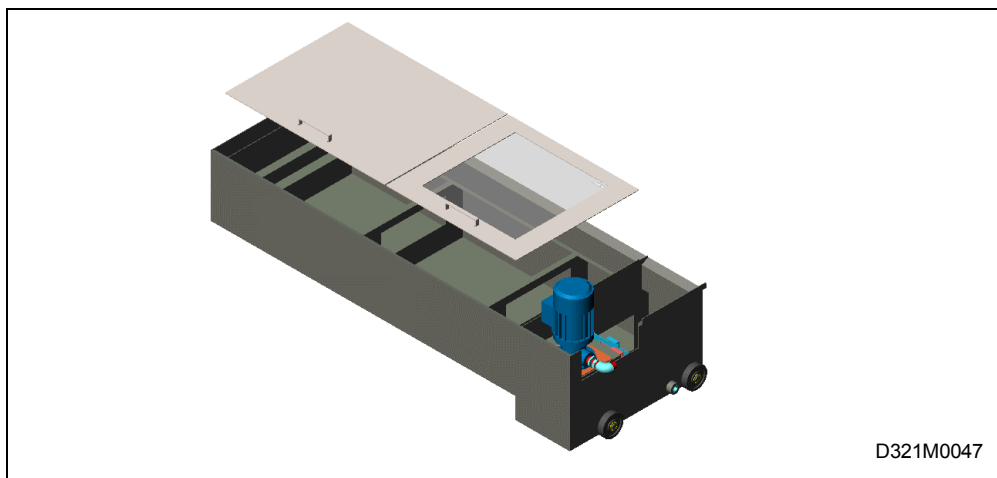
Очистка резервуара СОЖ(1/2)
